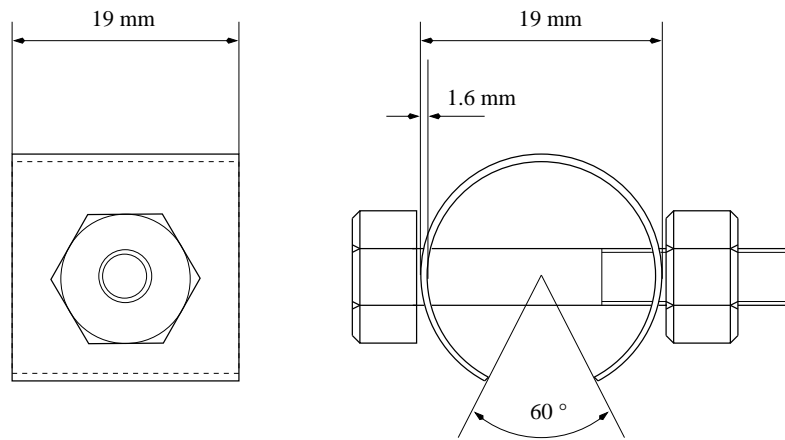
Probenabmessungen für C-Ring-Tests
